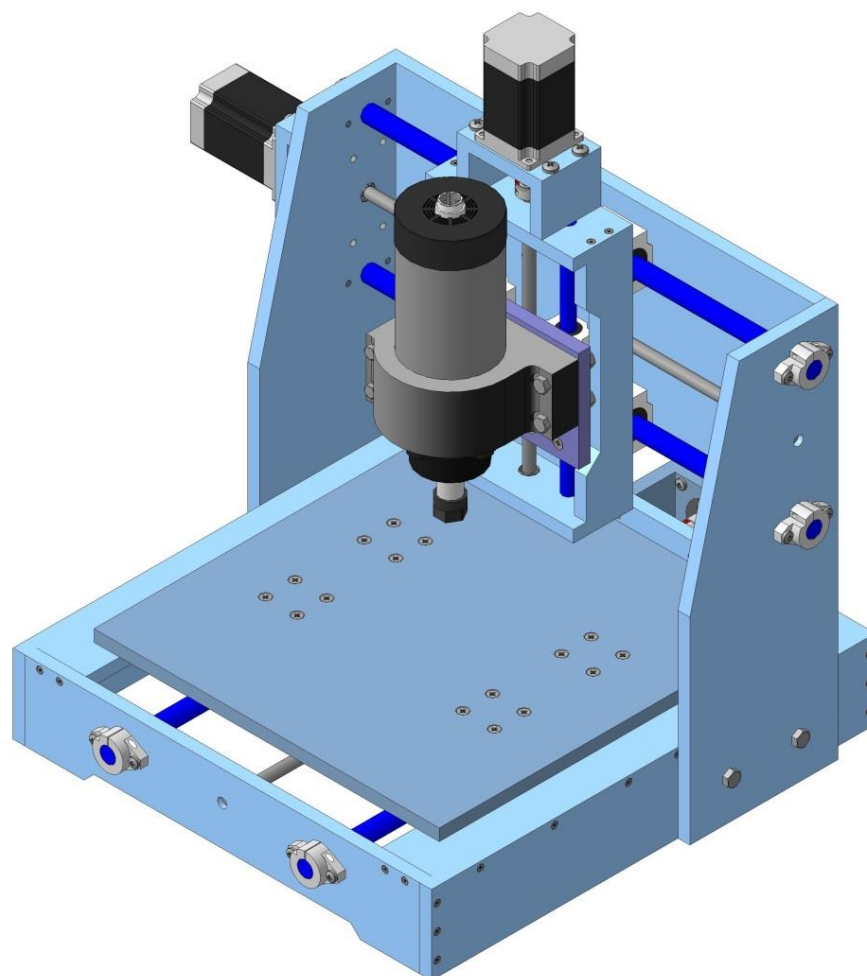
Вертикально-фрезерный станок с ЧПУ.
